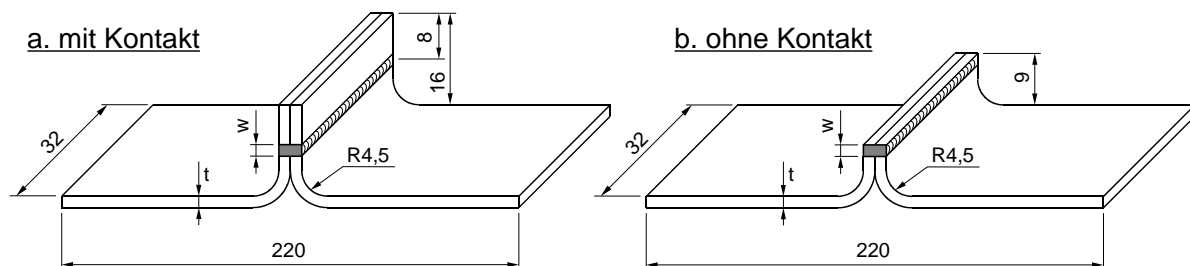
Geometrie der Schälzugproben, freie Länge 125 mm
